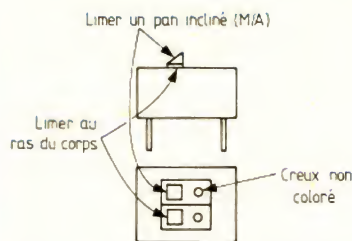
Usinage de l'interrupteur M/A (SECME, Intel DIL - 2 inters : 09 20 000 03).
